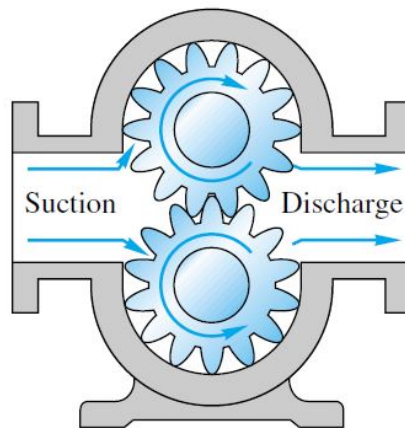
Funcionamento da bomba com engrenagem externa. Adaptado de [9].
